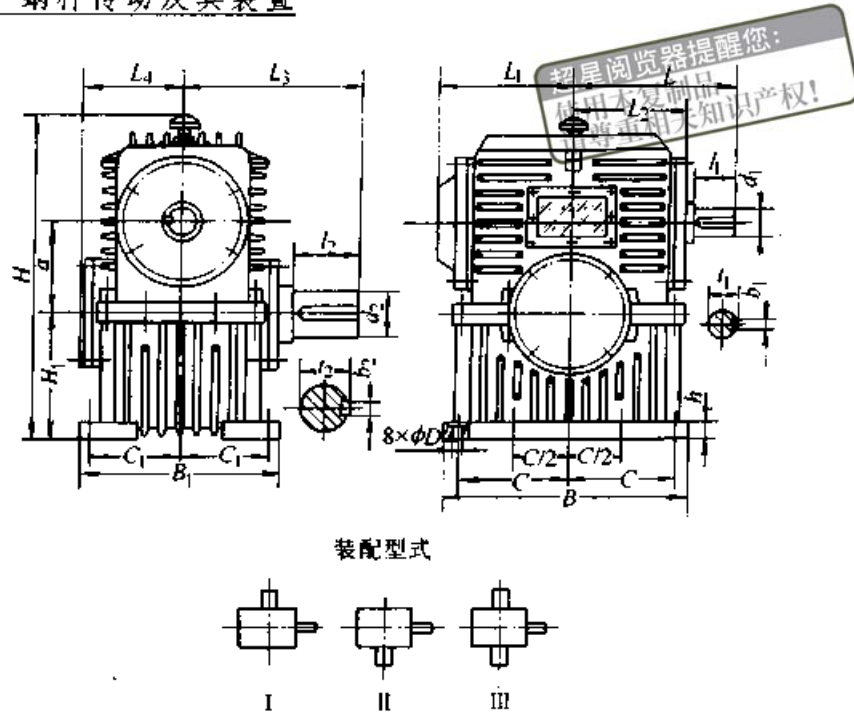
PWO 型减速器外形尺寸及装配型式 (剖分式)
